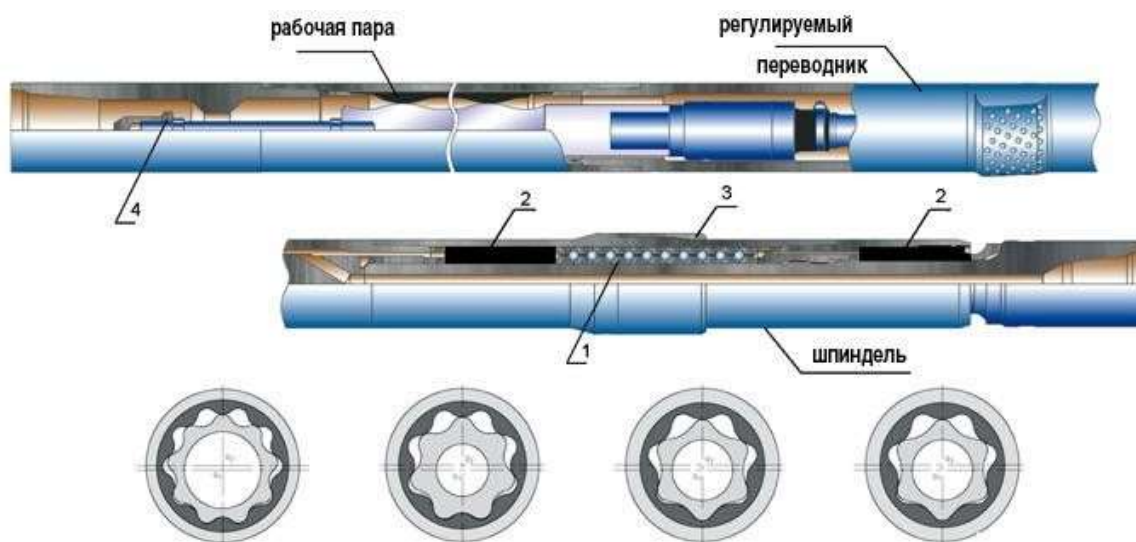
Общий вид винтового забойного двигателя:
